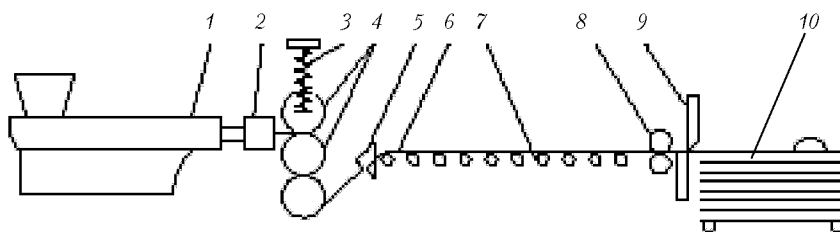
Технологическая схема агрегата для получения листов: 1 — экструдер; 2 — листовая головка; 3 — механизм для регулирования зазора между валками; 4 — гладильно-калибровочные валки каландра; 5 — ножи для обрезки кромок; 6 — лист; 7 — рольганг; 8 — тянущее устройство; 9 — гильотинный нож; 10 — штабель листов
